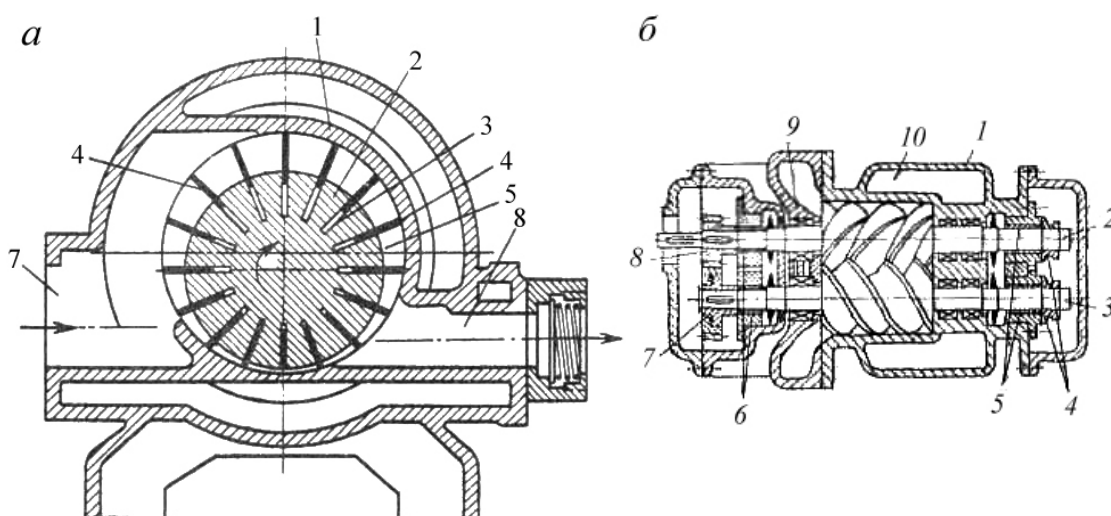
Схемы компрессоров: а – роторного пластинчатого: 1 – корпус; 2 – ротор; 3 – пластина; 4 – рубашка; 5, 7 – нагнетательный и всасывающий патрубки; б – винтового: 1 – корпус; 2 – ведущий винт; 3 – ведомый винт; 4 – упорный подшипник; 5, 6 – опорные подшипники; 7, 8 – синхронизирующие шестерни; 9 – уплотнение; 10 – полость для циркуляции охлаждающей жидкости
